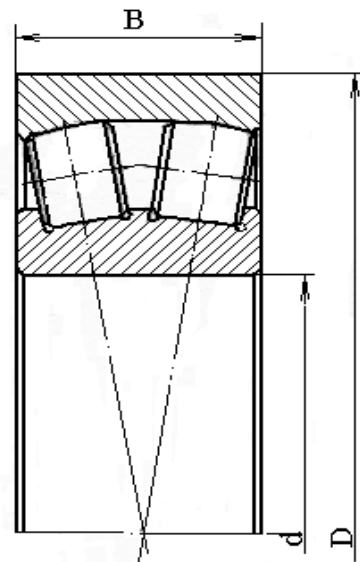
Подшипник роликовый радиальный, двухрядный, самоустанавливающийся с бочкообразными роликами
